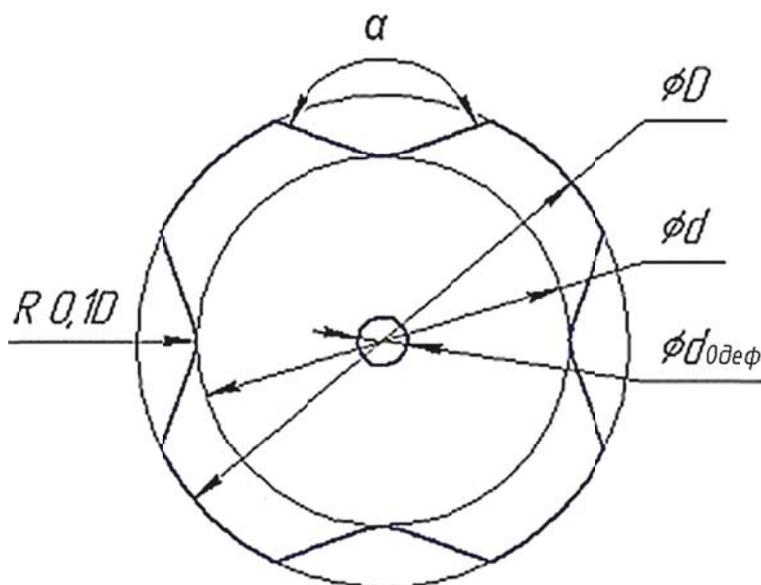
Схема поперечного сечения заготовки с вогнутым поперечным сечением
